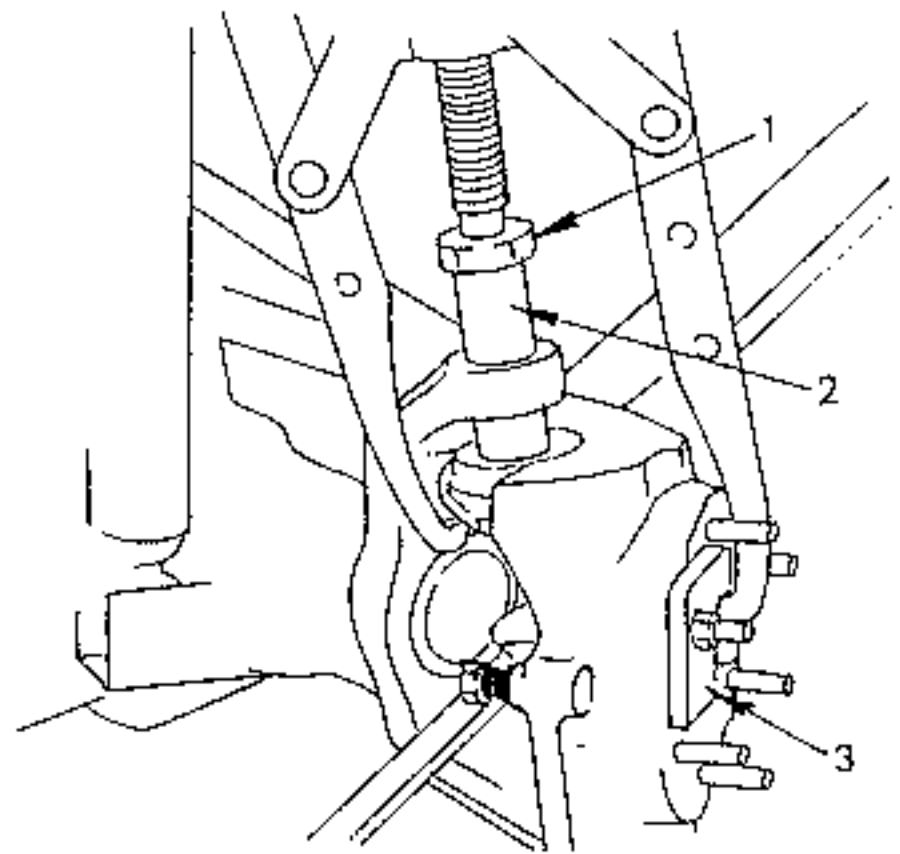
Einbau eines Achsgelenks. Die gezeigten Spezialwerkzeuge sind zum Eindrücken des oberen Kugelbolzens erforderlich.
